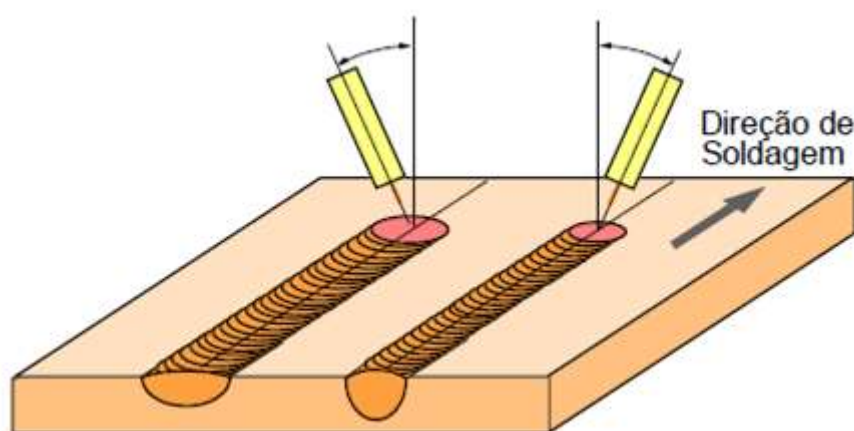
Efeito da inclinação do eletrodo no formato do cordão – Fonte: Trabalho prático UFMG – Técnica operatória de soldagem SAW
